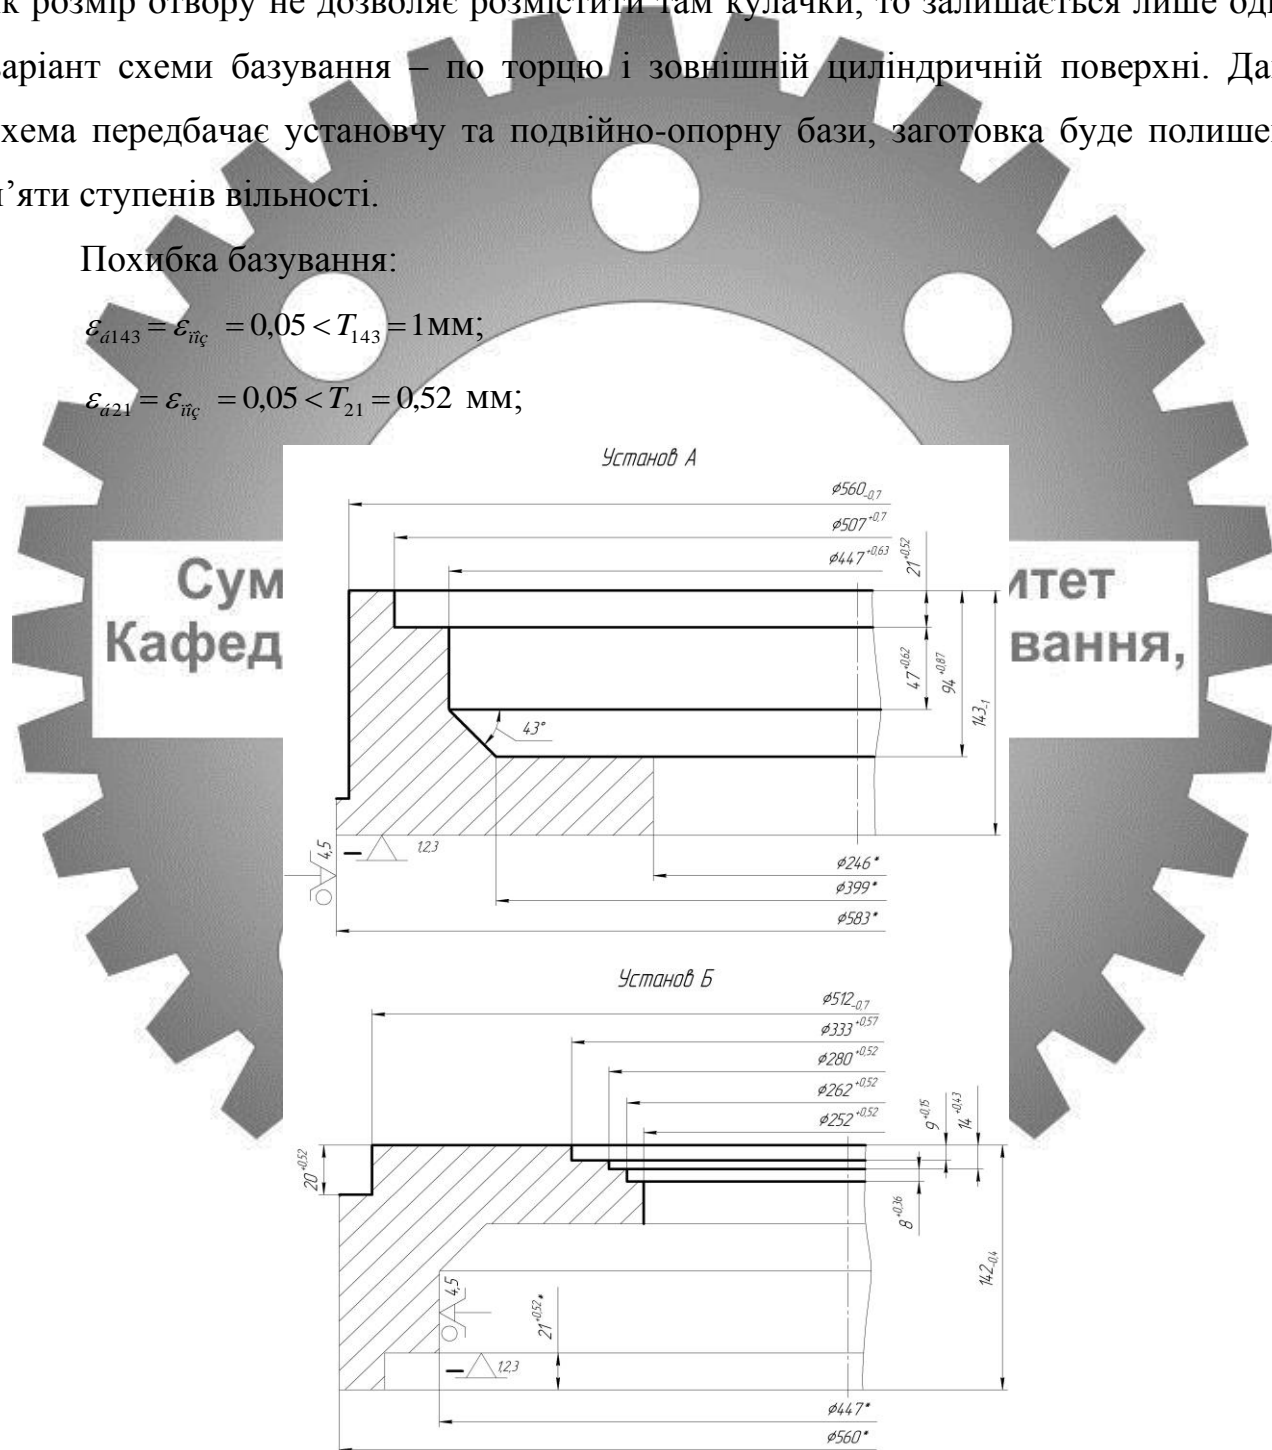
Схема базування заготовки на токарній операції (перший варіант)
